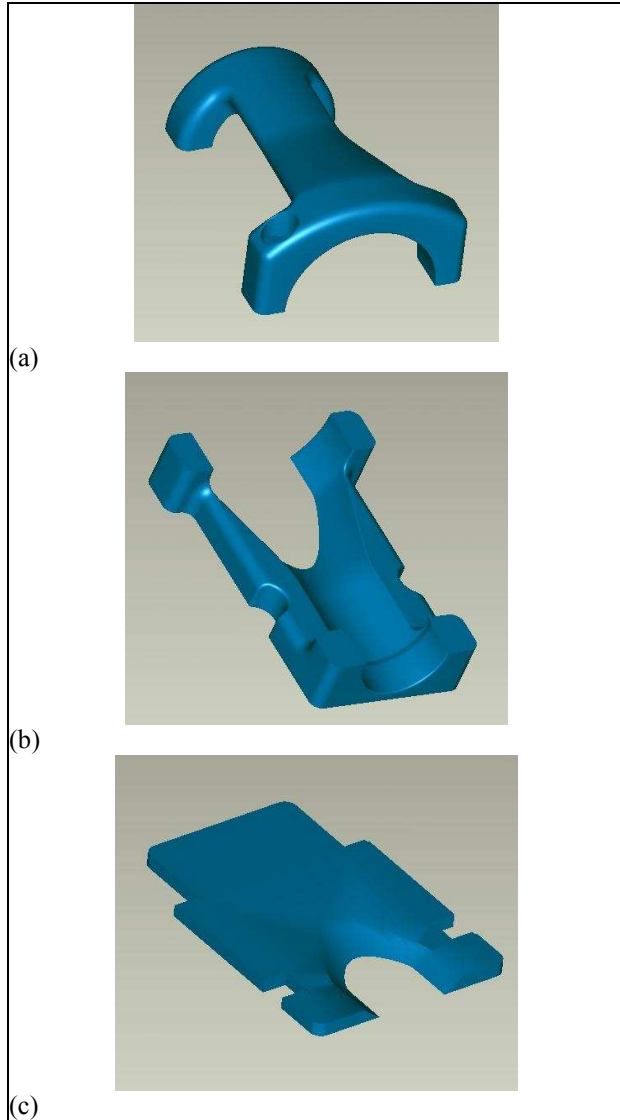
Partes del soporte portaherramienta. (a) pieza A, (b) pieza B y (c) pieza C.
